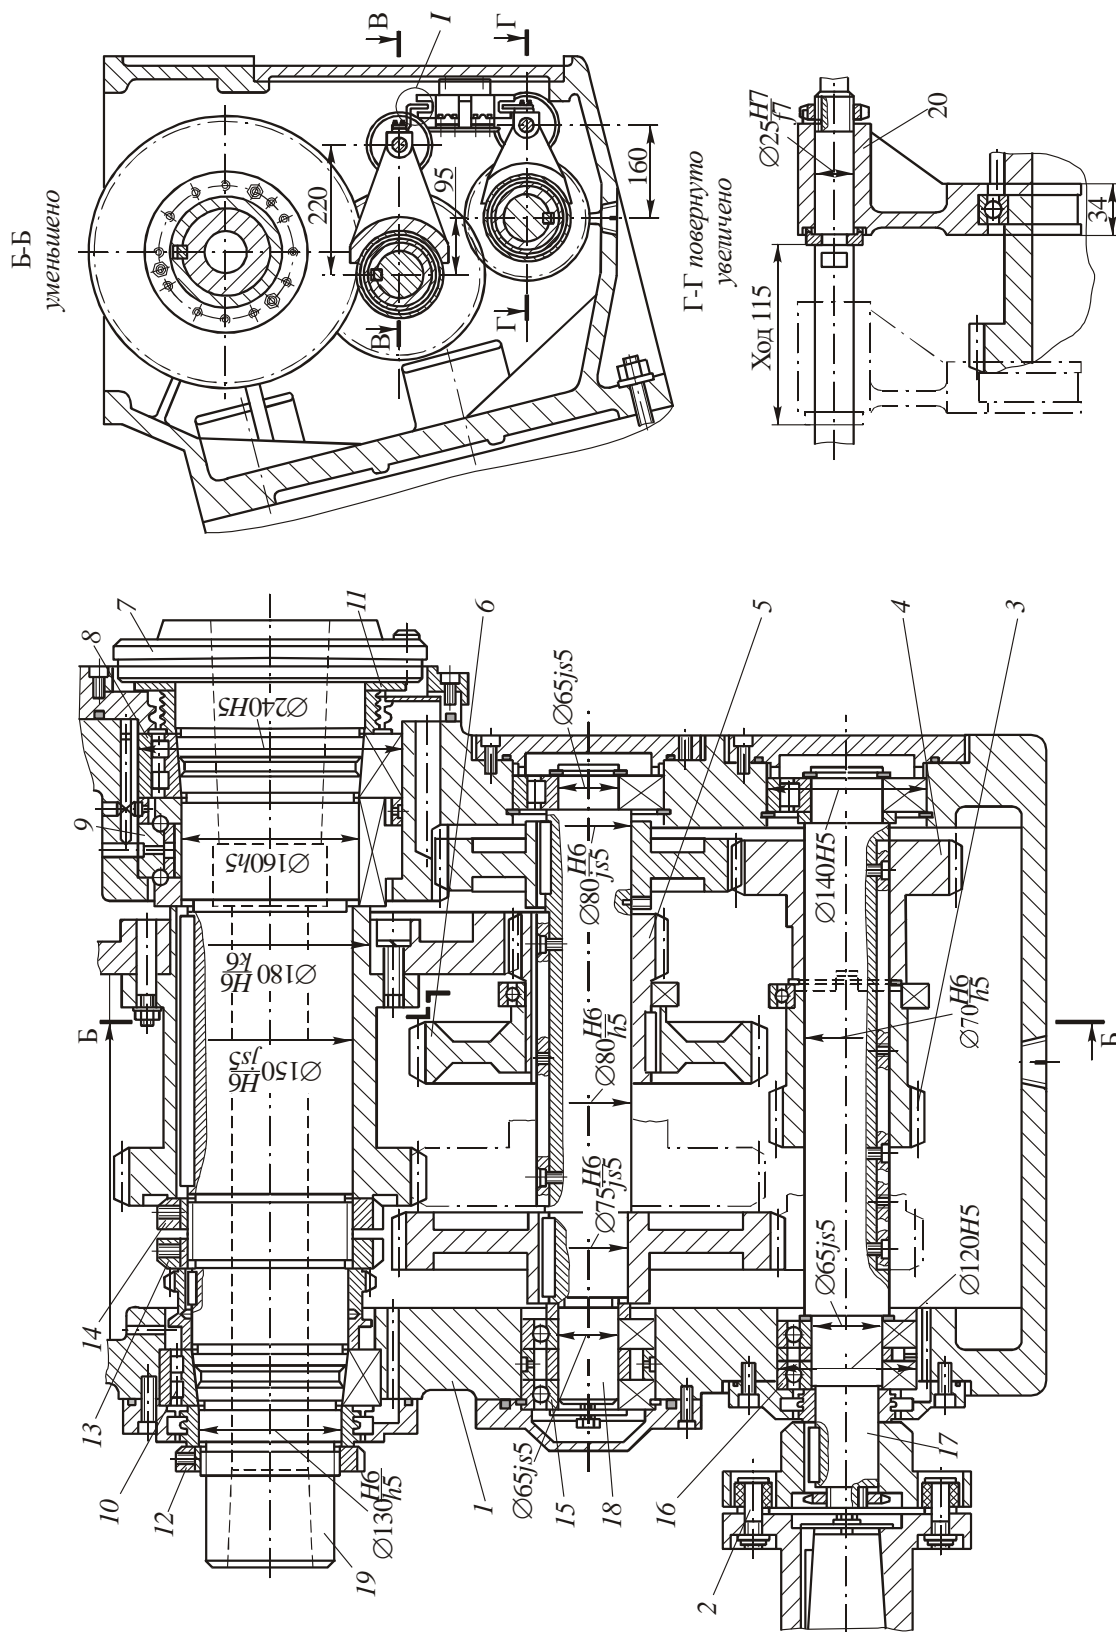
Шпиндельная коробка токарного станка с ЧПУ
